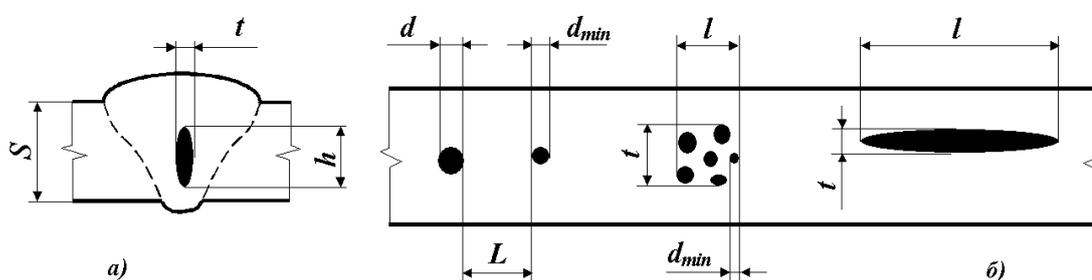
Схематическое изображение сварного шва и определение размеров дефектов: а) вид в сечении; б) вид в плане [7]:
